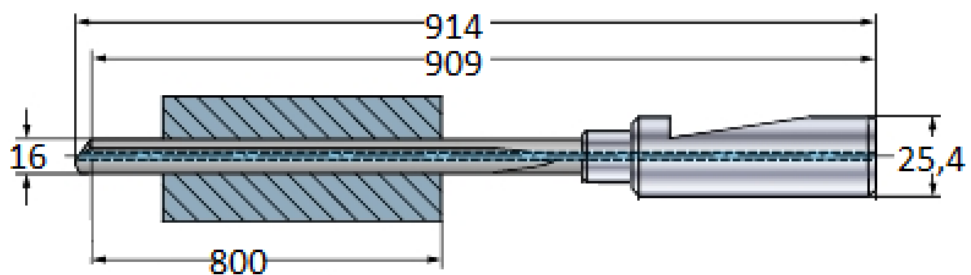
Ружейное сверло Sandvik Coromant A428.91-06250-36-205K15
